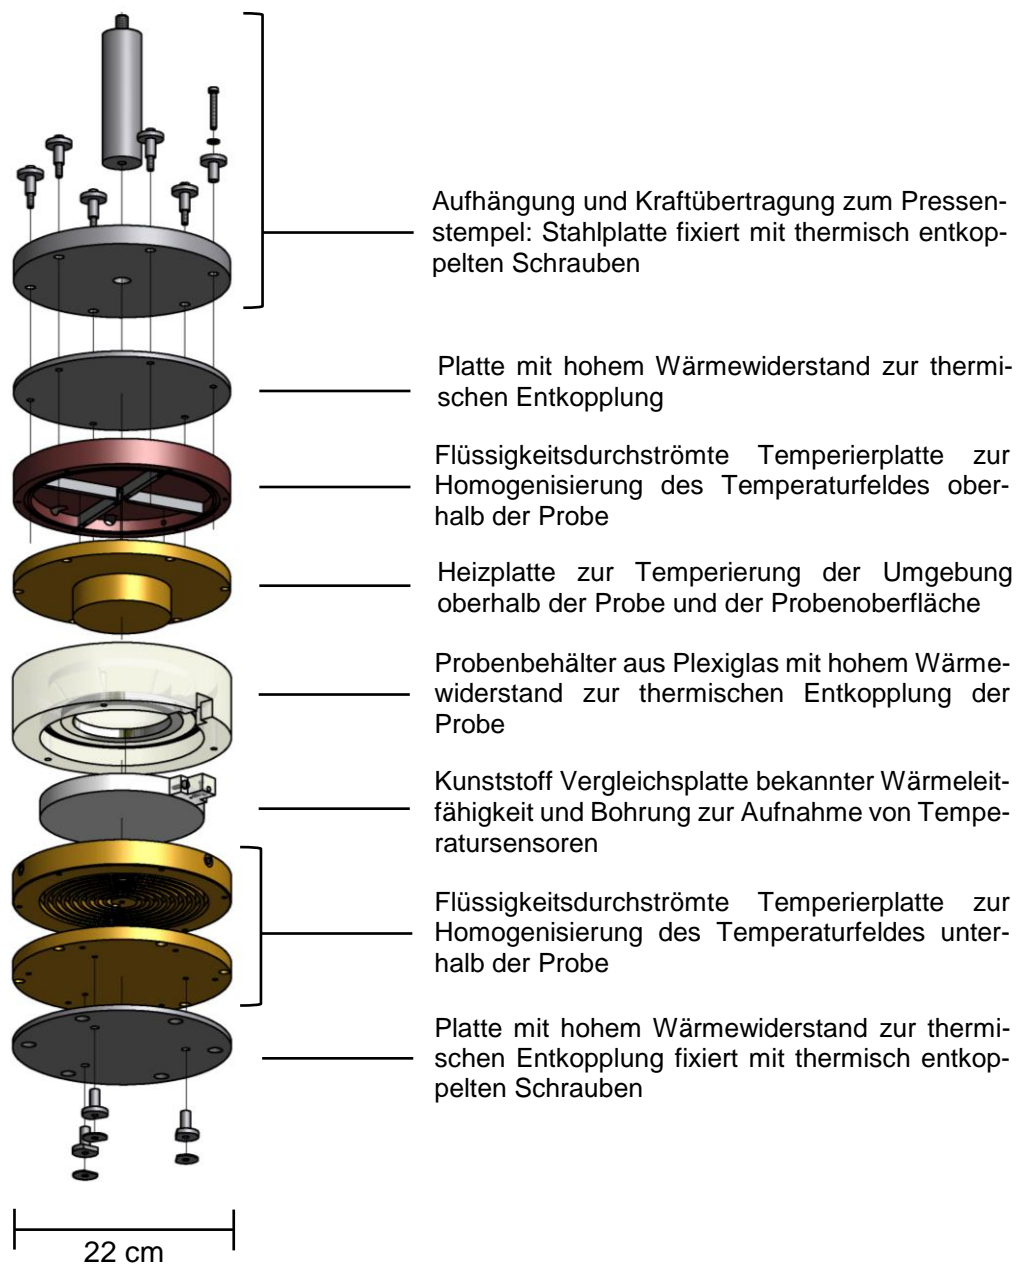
Explosionszeichnung des Prüfeinsatzes
